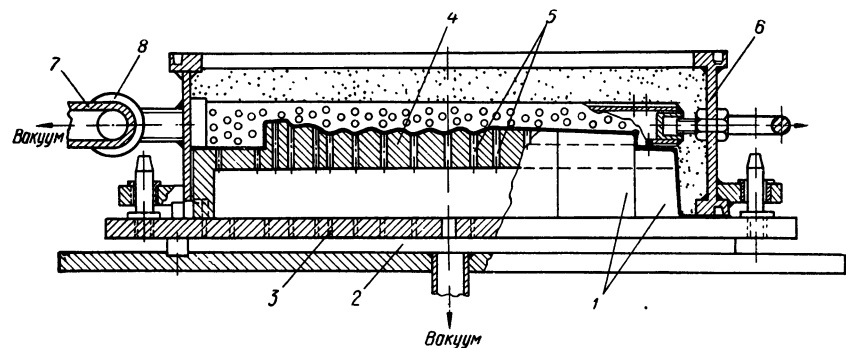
Схема модельно-опочной оснастки в разрезе с заполненной песком полуформой для гильз двигателя СМД-14.
